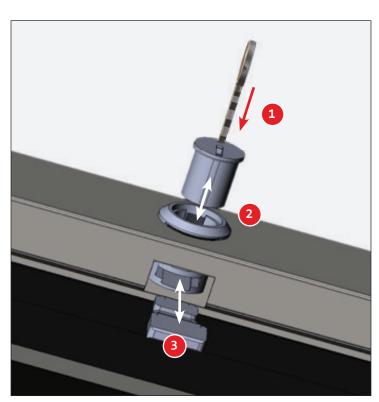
Vue de dessous du retrait/de l'installation des composants.
